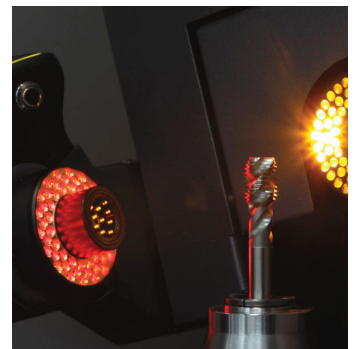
Mit einem Schwenkbereich von -30° bis 30° eliminiert »orthoScan« steigungsbedingte Verzerrungen bei der Messung von Gewindewerkzeugen.
